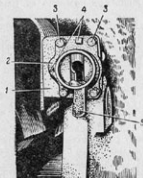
Установочное приспособление пулемета ДТМ, спаренного с танковой пушкой:
